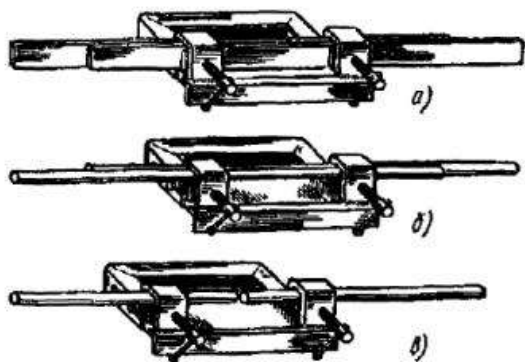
Закрепление свариваемых стальных полос и стержней:
